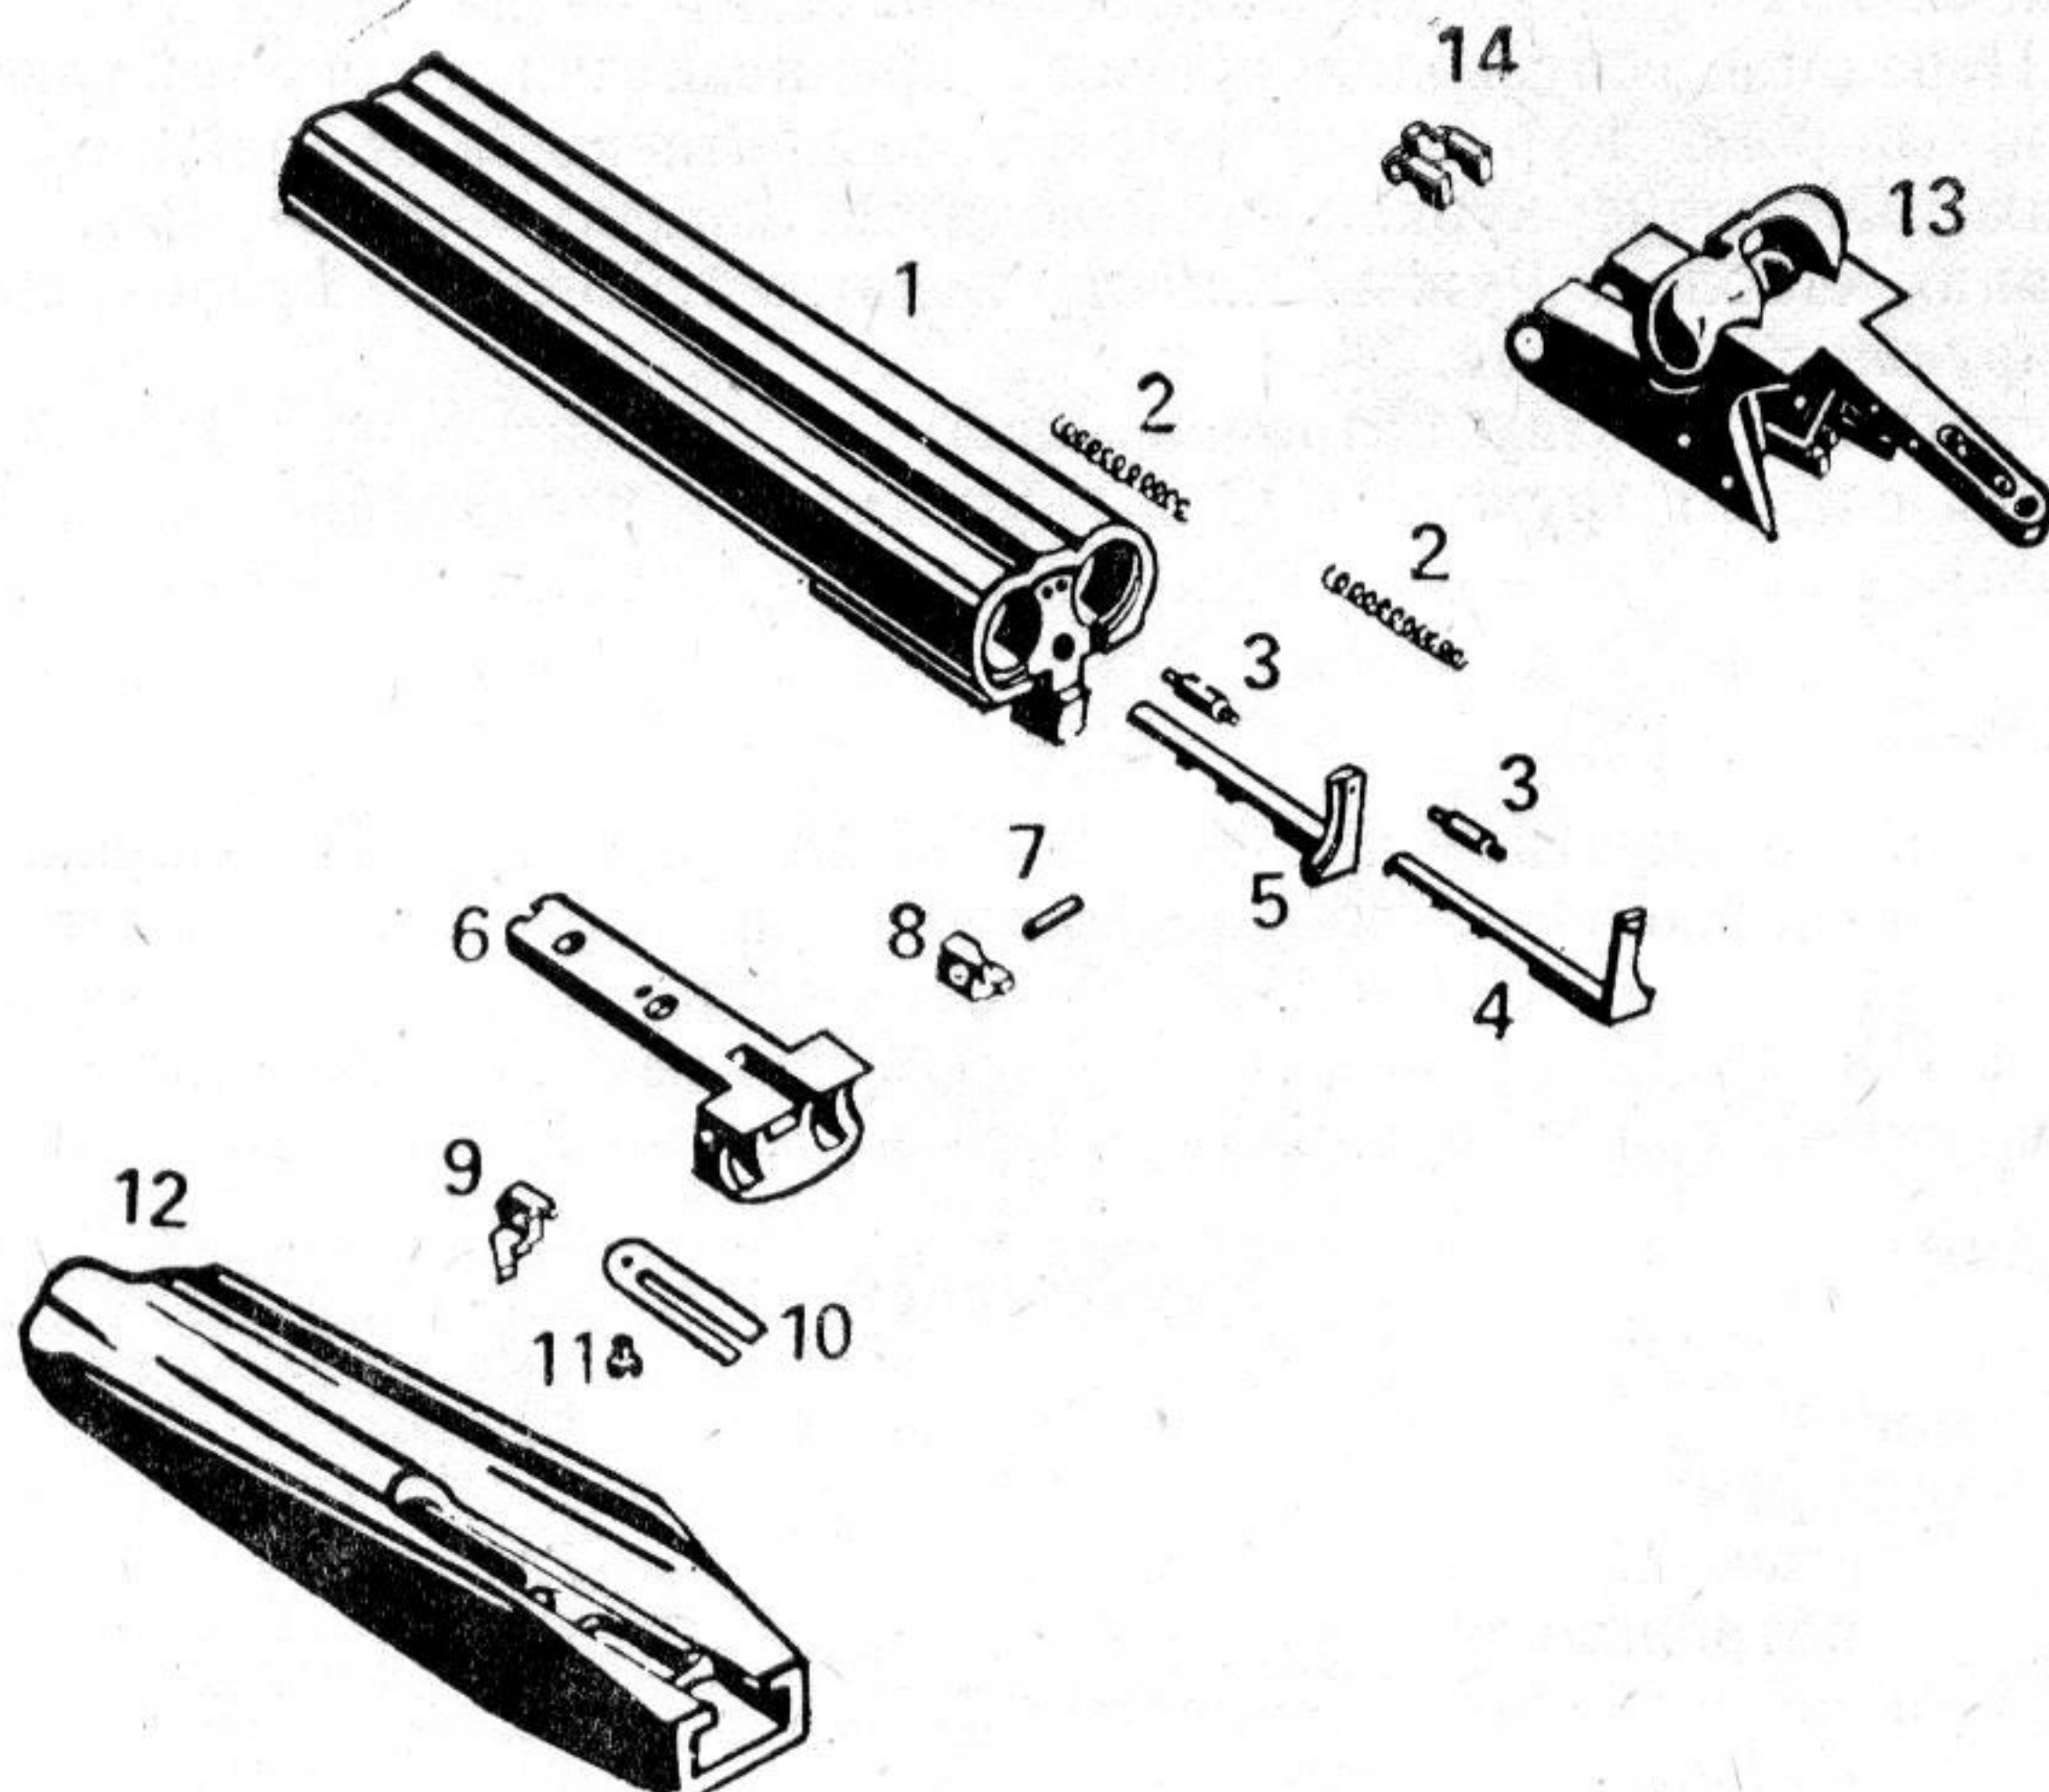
Детали ружья ИЖ-43 ЕМ:
